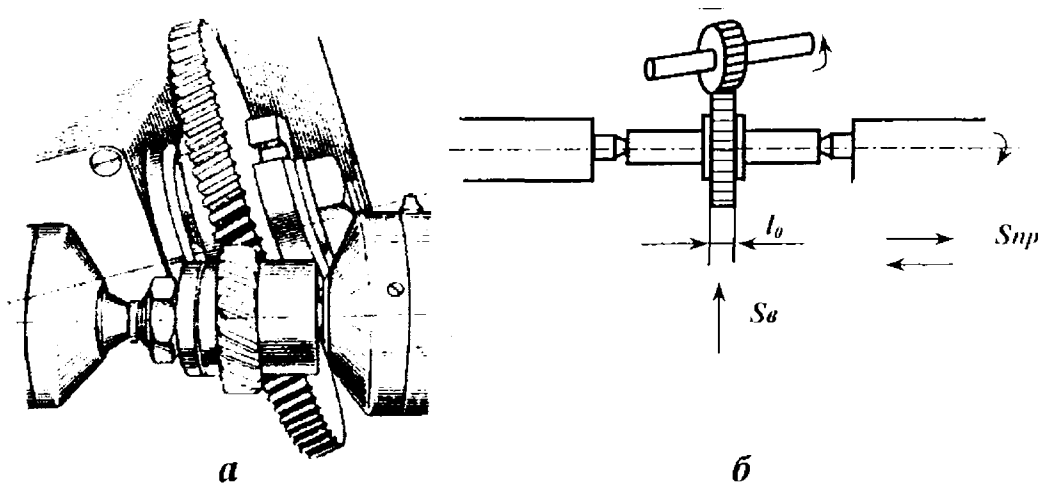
Шевингование цилиндрического зубчатого колеса дисковым шевером: *a* – общий вид (подача продольная); *б* – схема шевингования с вертикальным перемещением стола станка
